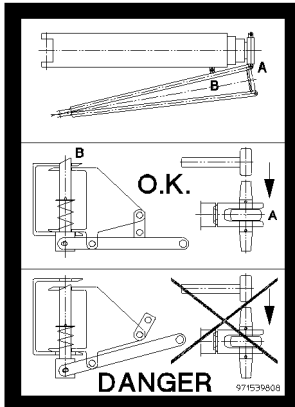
Indicação de alerta sobre despinagem da lança auxiliar na cabeça da roldana
